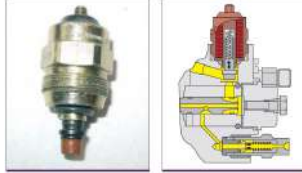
Componentes bomba rotativa de embolo axial. Bosch
